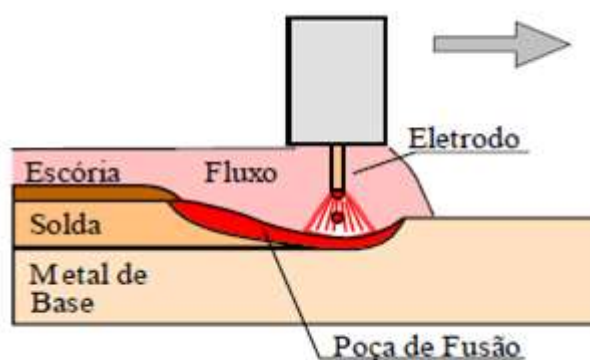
Esquema de soldagem – Fonte: Trabalho prático UFMG – Técnica operatória de soldagem SAW
